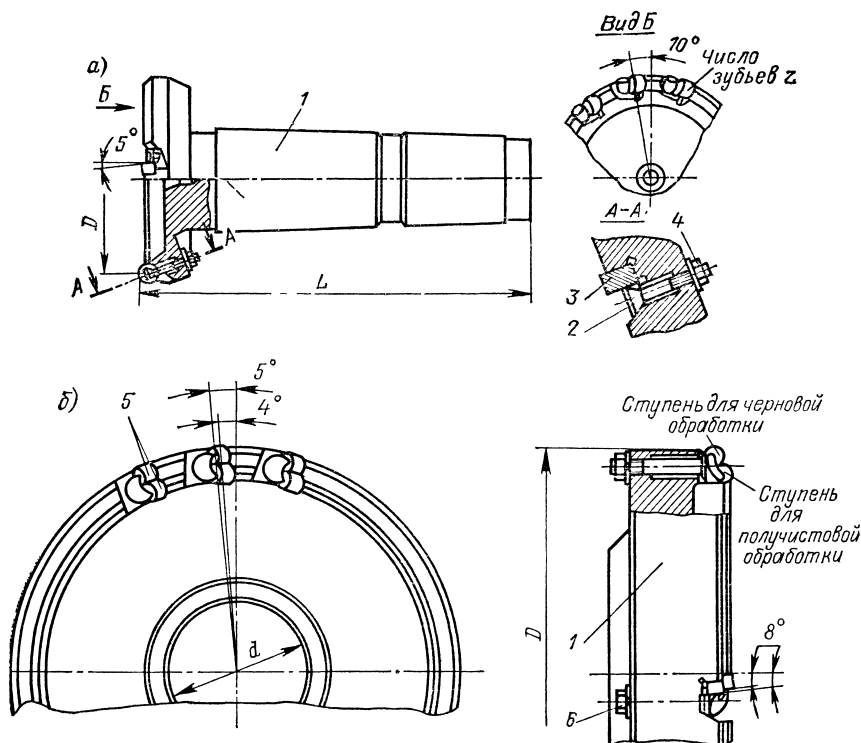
Фрезы торцовые с механическим креплением круглых пластин из композита: а — концевая; б — насадная двухступенчатая:
